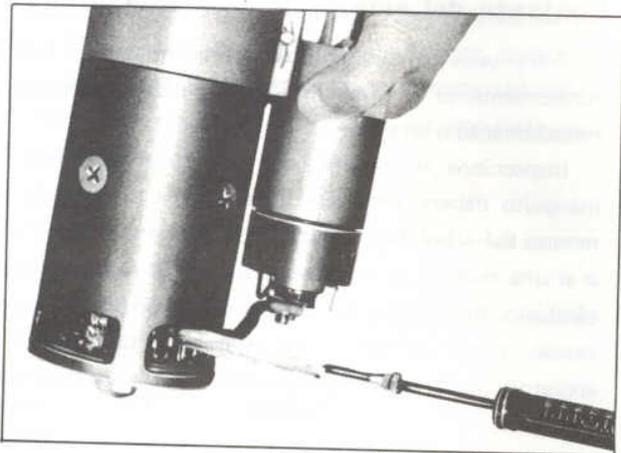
Inspección de la presión del resorte de la escobilla
